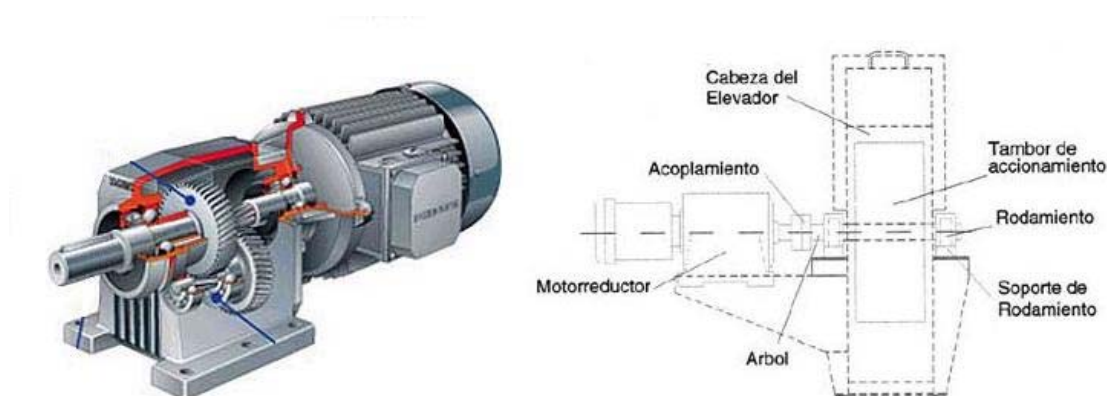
Acoplamiento del motorreductor al tambor accionador.
